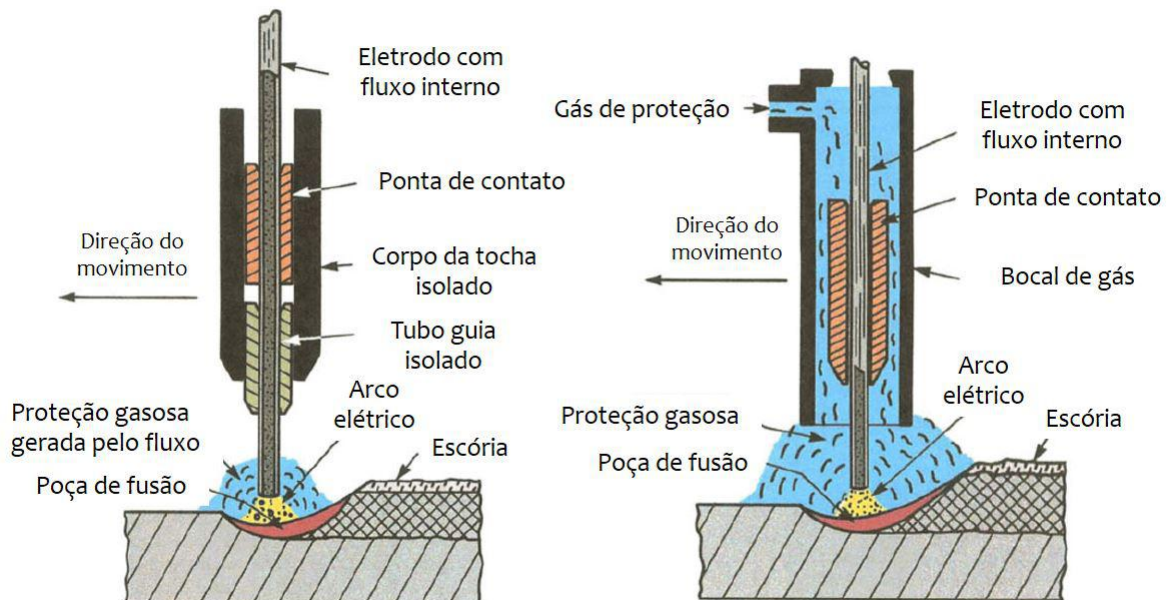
Desenho esquemático de uma operação de soldagem com FCAW (Adaptado de [28]).
